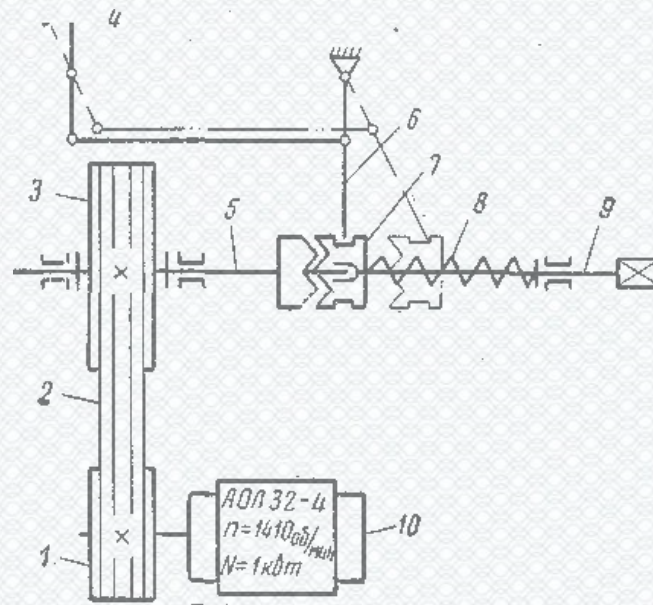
Схема механізму гайковерту для гайок коліс
